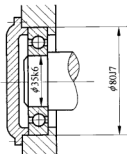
轴颈和外壳孔公差在图样上的标注
